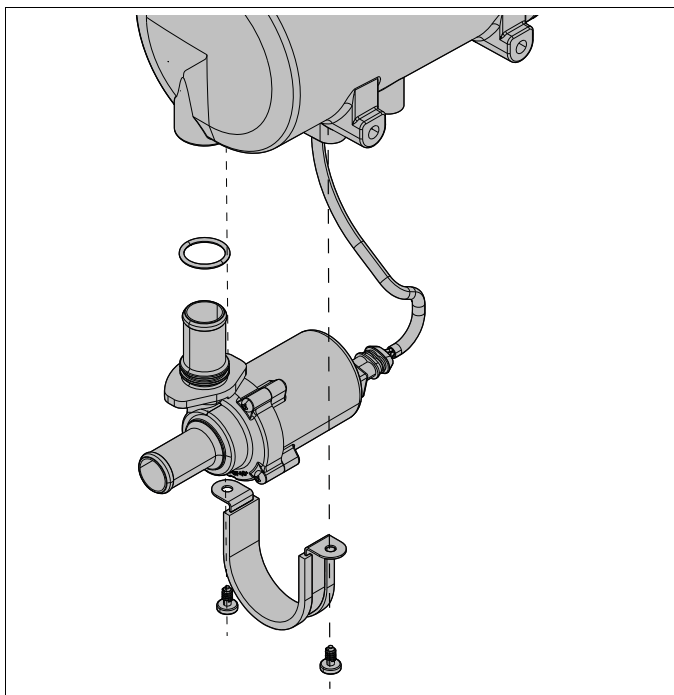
Wechsel der Kühlmittelpumpe U4840
